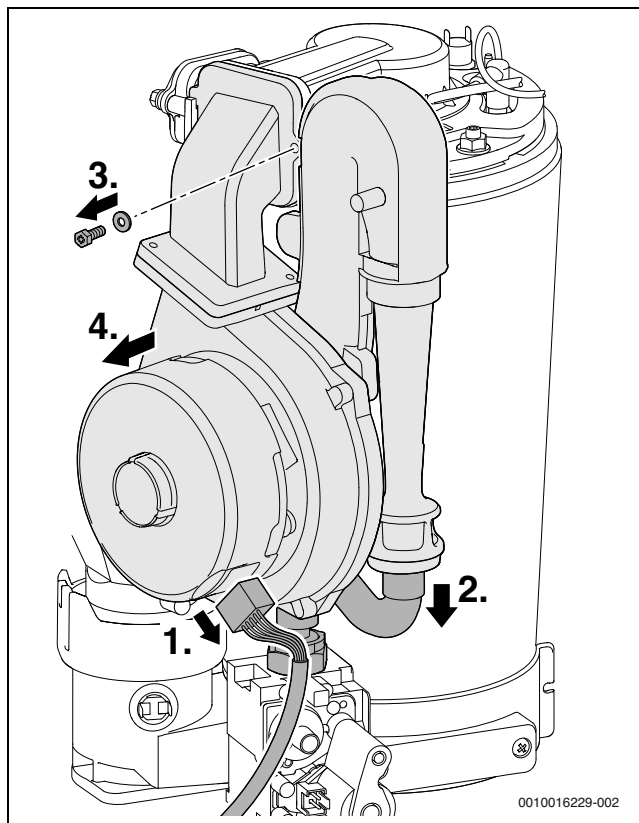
Desmontar o ventilador com dispositivo de mistura
